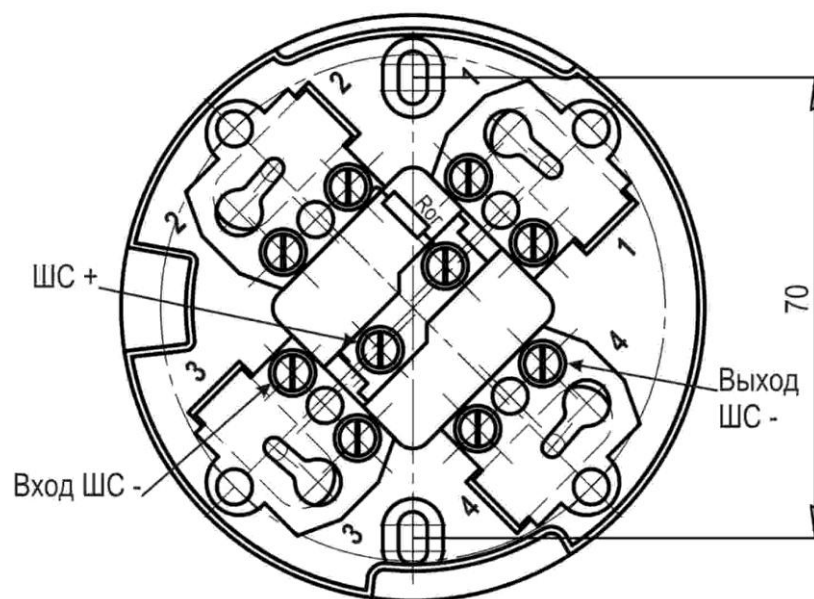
Розетка извещателя. Общий вид и расположение контактов
